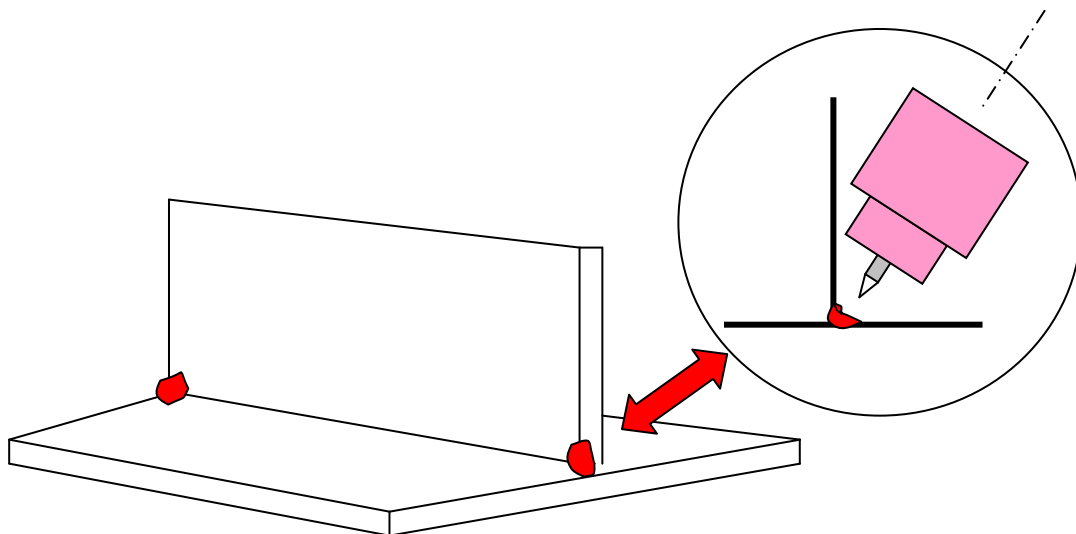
Punteado para obtener el ensamble de soldadura de filete entre placas.
